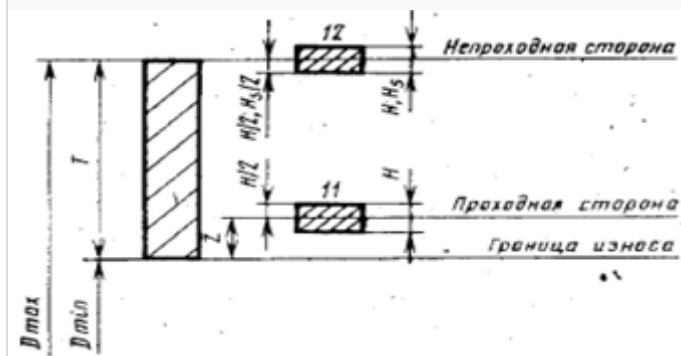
Схема полей допусков калибра-пробки для квалитетов 9-17
